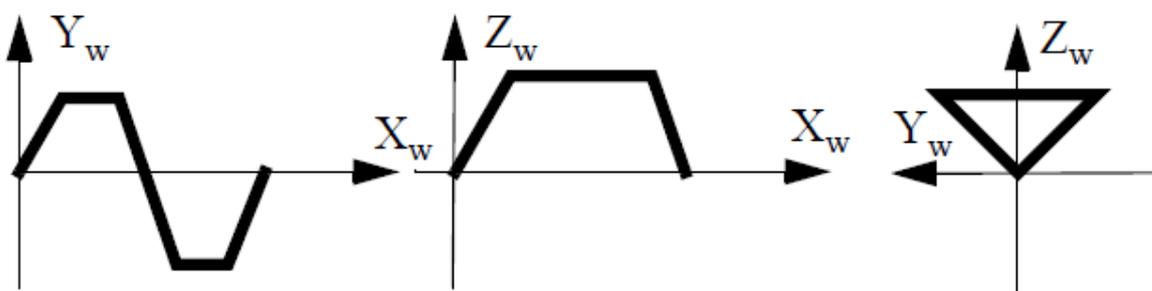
Tecimento - Movimentos realizados quando a forma zigzag é utilizada
